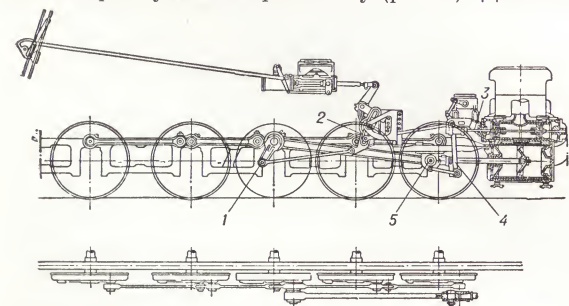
Общий вид и план кулисного механизма паровоза: 1 — контркривошип; 2 — кулиса; 3 — скалка золотника; 4 — маятник; 5 — ползун.
